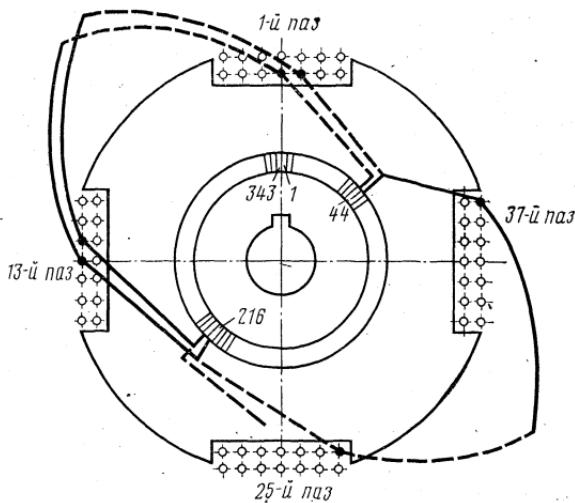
Схема соединения обмотки якоря с коллекторными пластинами электродвигателя НБ-431А
